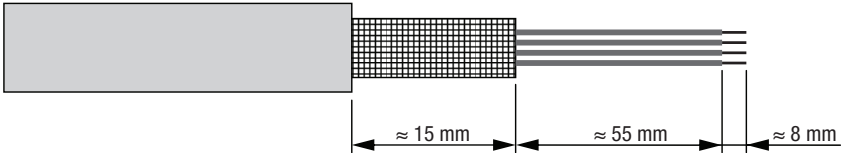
Confección del cable para el módulo de bornes MK 301
